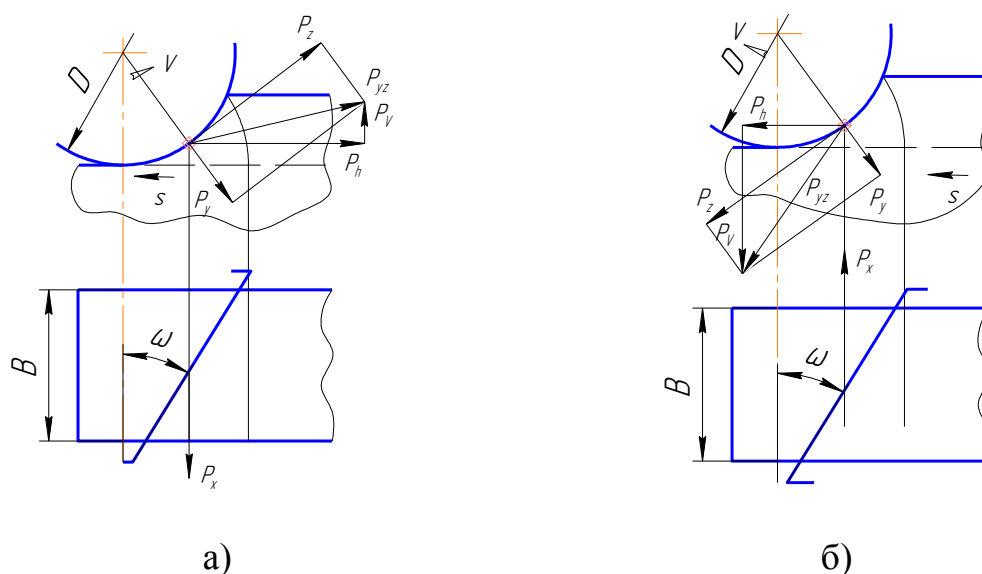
Складові сили різання при фрезеруванні циліндричною фрезою: а – при зустрічному фрезеруванні (проти подачі); б – попутному (у напрямку подачі)
